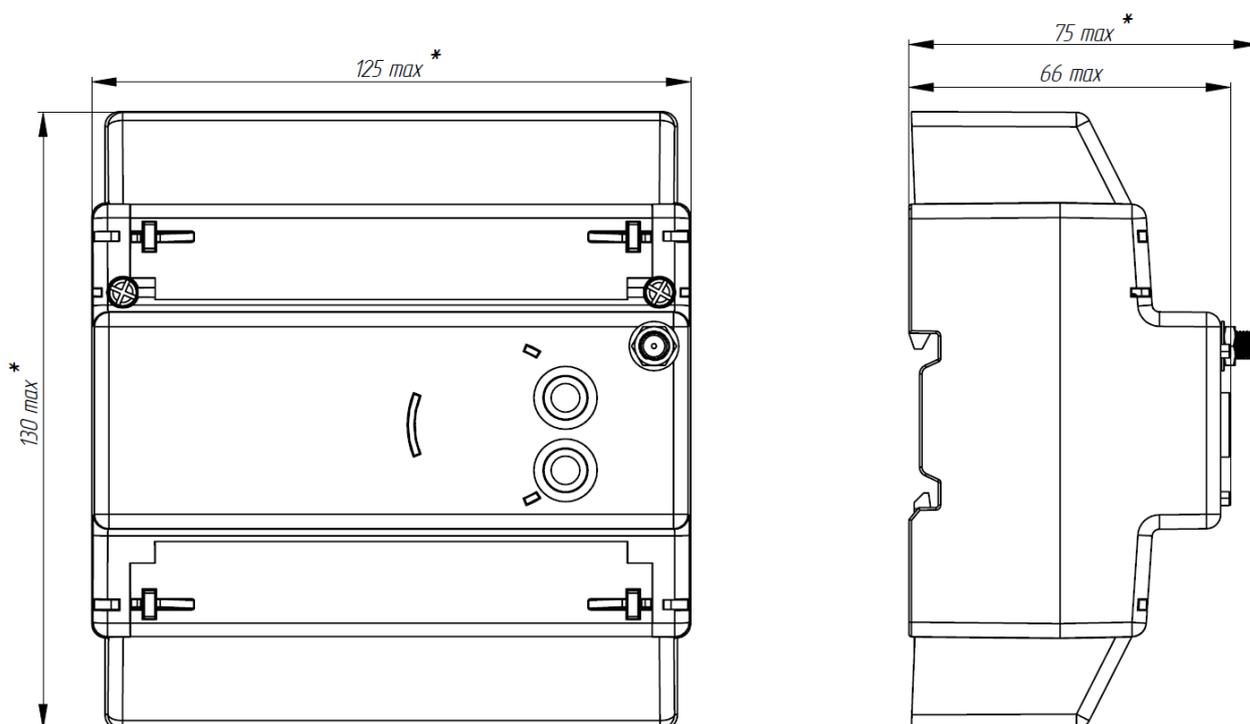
Корпус 7мТН35 со стандартными клеммными крышками (\* габаритные размеры)
